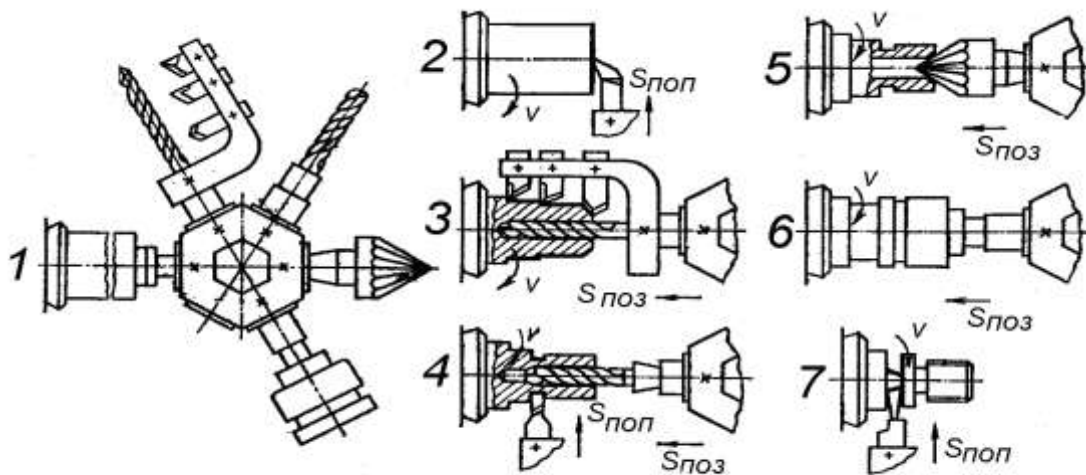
Схеми обробки поверхнь заготовки на револьверному верстаті
